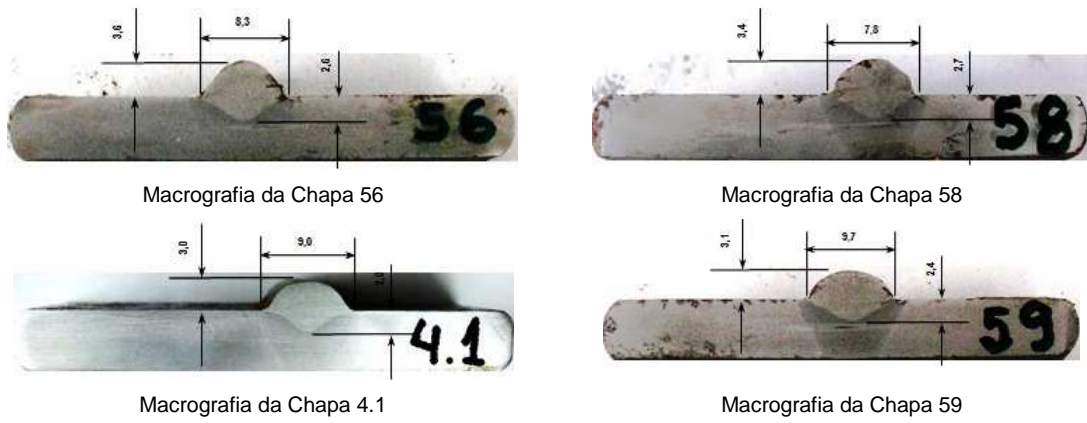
Macrografias com altura do reforço (r), largura do cordão de solda (b) e a penetração das soldas com Ar+4% H_2 .
